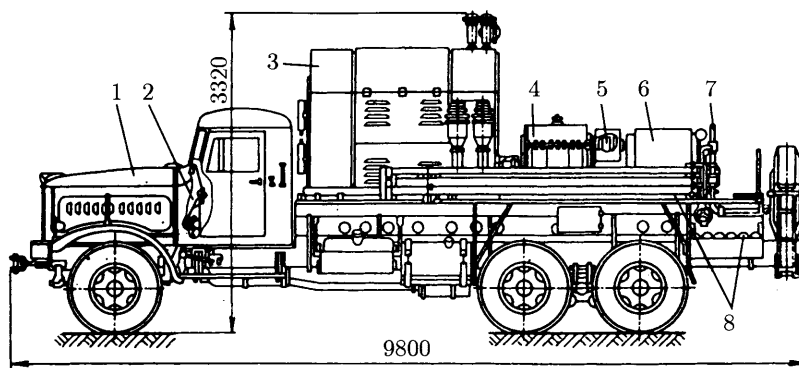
Насосная установка УН-1-630 на 700А: 1 – автошасси КрАЗ-257; 2 – пост управления; 3 – силовой агрегат; 4 – коробка передач ЗКПМ; 5 – зубчатая муфта; 6 – насос 4Р-700; 7 – напорный трубопровод; 8 – вспомогательный трубопровод
